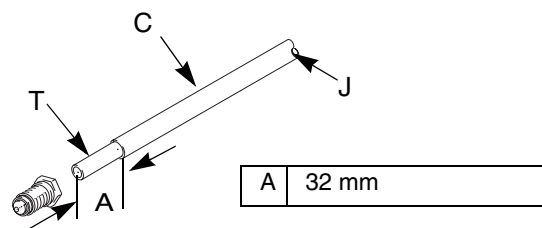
Dimensions des flexibles pour produits à base aqueuse (sur le pistolet)
